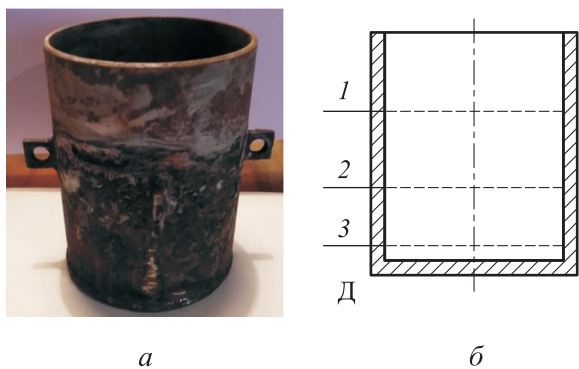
Внешний вид корпуса лабораторного реактора после проведения 40 активаций (а) и схема его деления на условные участки (б)
